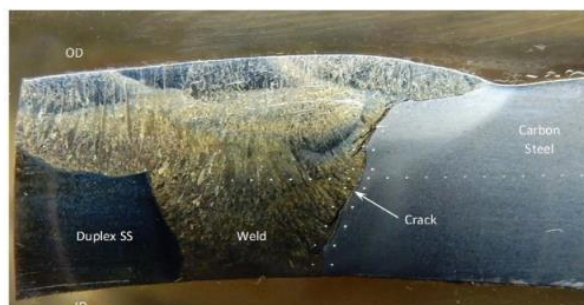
Sección transversal de la soldadura disímil acero dúplex 2205/acero al carbono [21].
